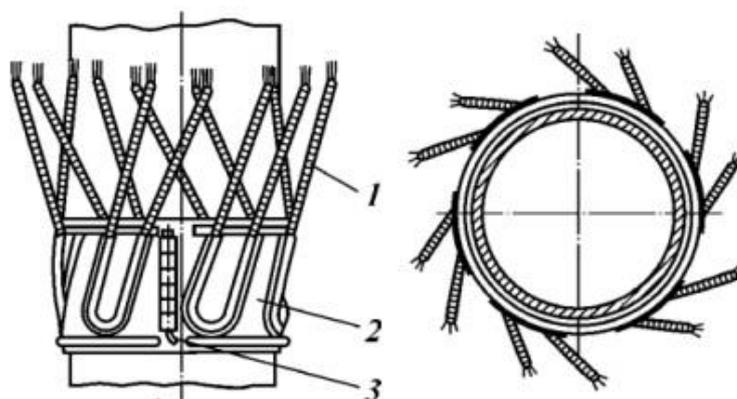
Скребок разъемный типа СК: 1 – пружинная стальная проволока; 2 – накладки; 3 – корпус
